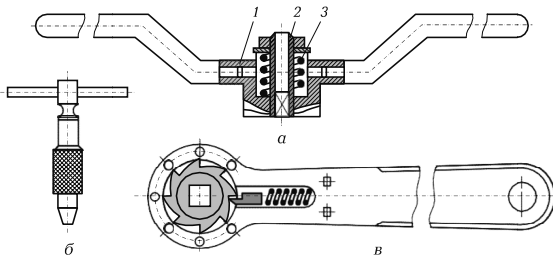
Воротки: а – запобіжний: 1 – корпус; 2 – втулка; 3 – пружина; б – торцевий; в – з тріскачкою
